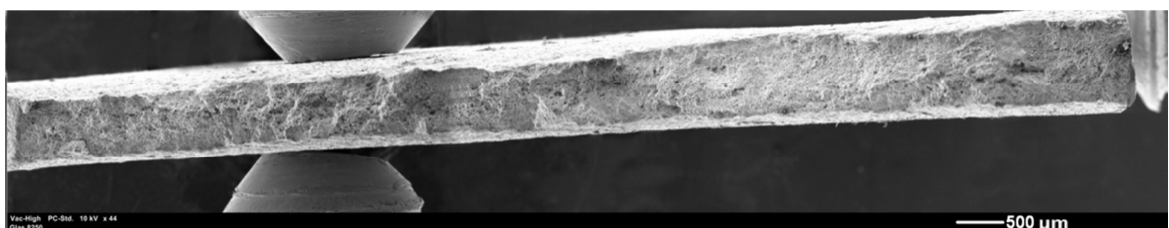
REM Übersichtsaufnahme der Bruchfläche einer EN AW-6016-T4 Zugprobe
